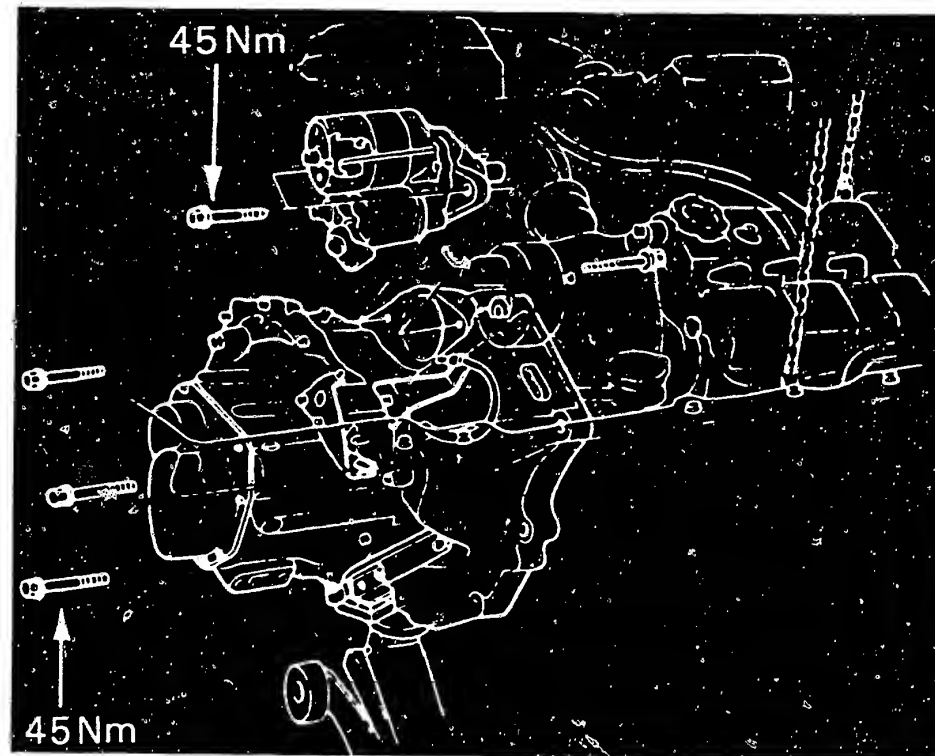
Ausbau des Getriebes: Dazu ist der Motor an eine Motorstütze oder einen Kran zu hängen. Die Getriebeschrauben (Pfeile) sind mit 45 Nm festzuziehen.
